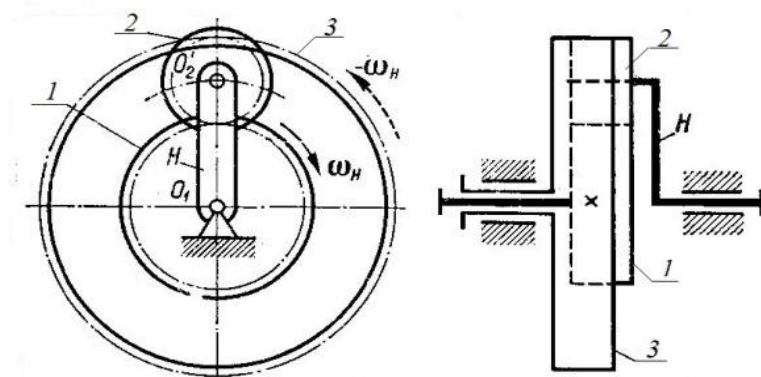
Сателлитный механизм с цилиндрическими колесами:
